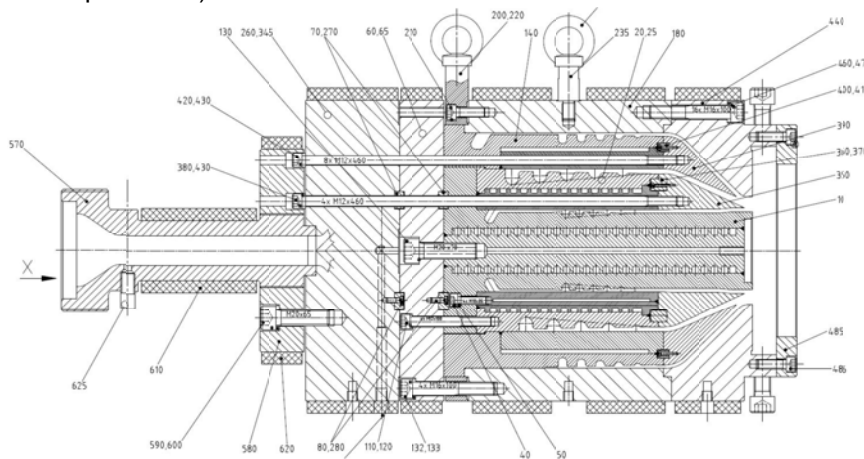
ETA Coextrusionswerkzeug mit 2-fach Temperierung und integrierter Isolierung
